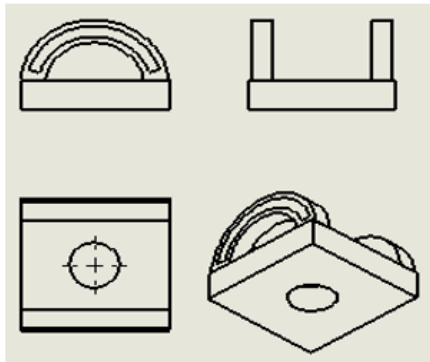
Órgão terminal: Vistas lateral, frontal, superior e isométrica.
